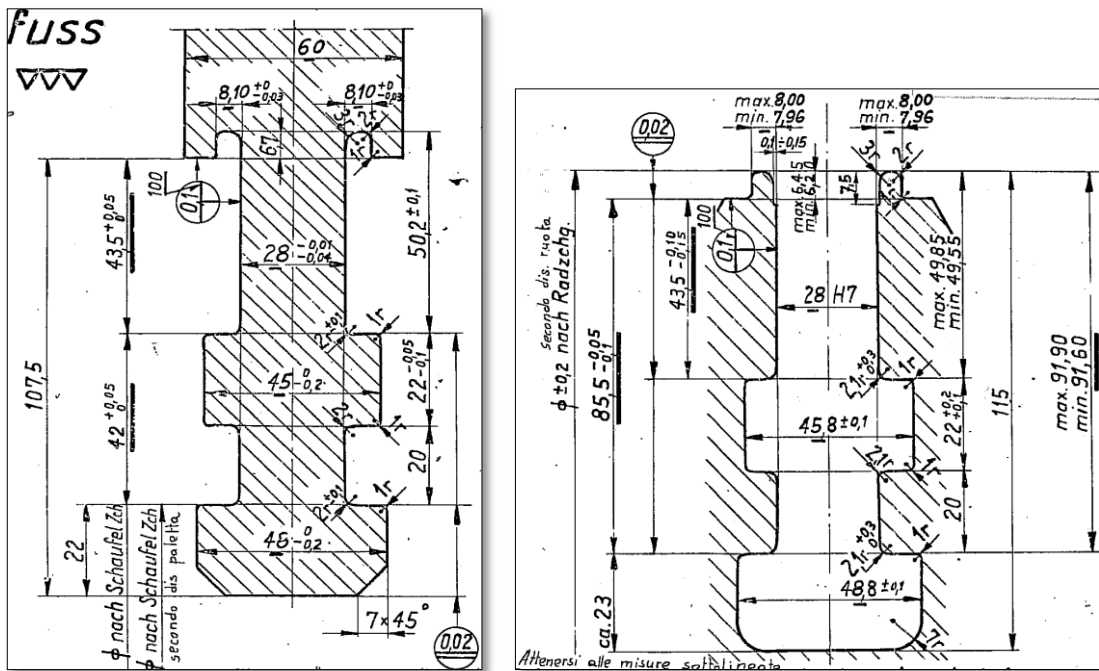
dimensioni del piede palare e della cava sul disco del 8° stadio della turbina n° 2.
